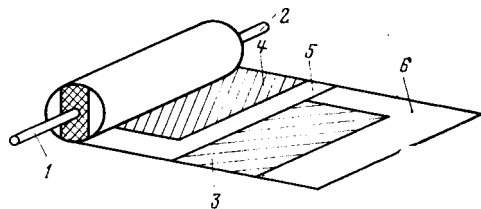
Цилиндрический конденсатор с торцевыми контактами
